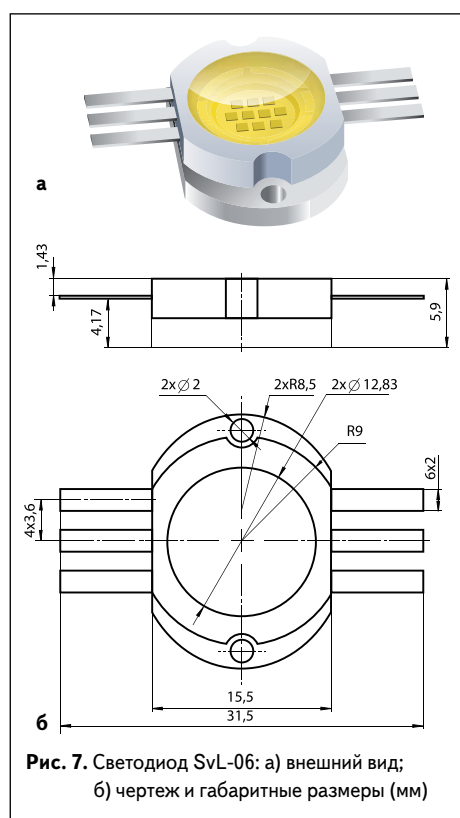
Светодиод SvL-06: а) внешний вид; б) чертеж и габаритные размеры (мм)
